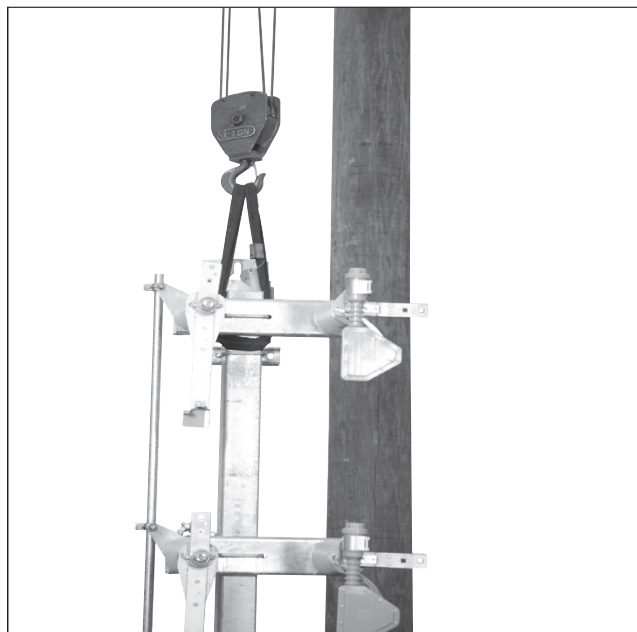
El interruptor de fase sobre fase mostrado en la posición Abierto para mejor la visibilidad de la pieza soldada de montaje. Ice el interruptor con las cuchillas en la posición Cerrado.
